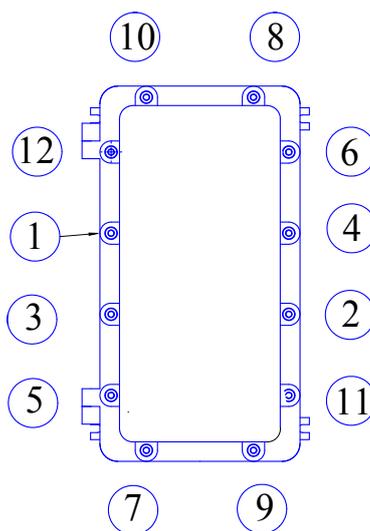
Порядок закручивания винтов крышки газоанализатора (вид спереди).
